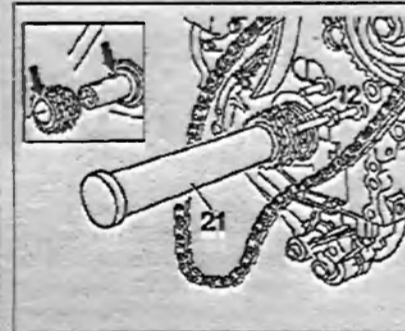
С помощью пробойника 21 установите новую звездочку коленчатого вала 12.
